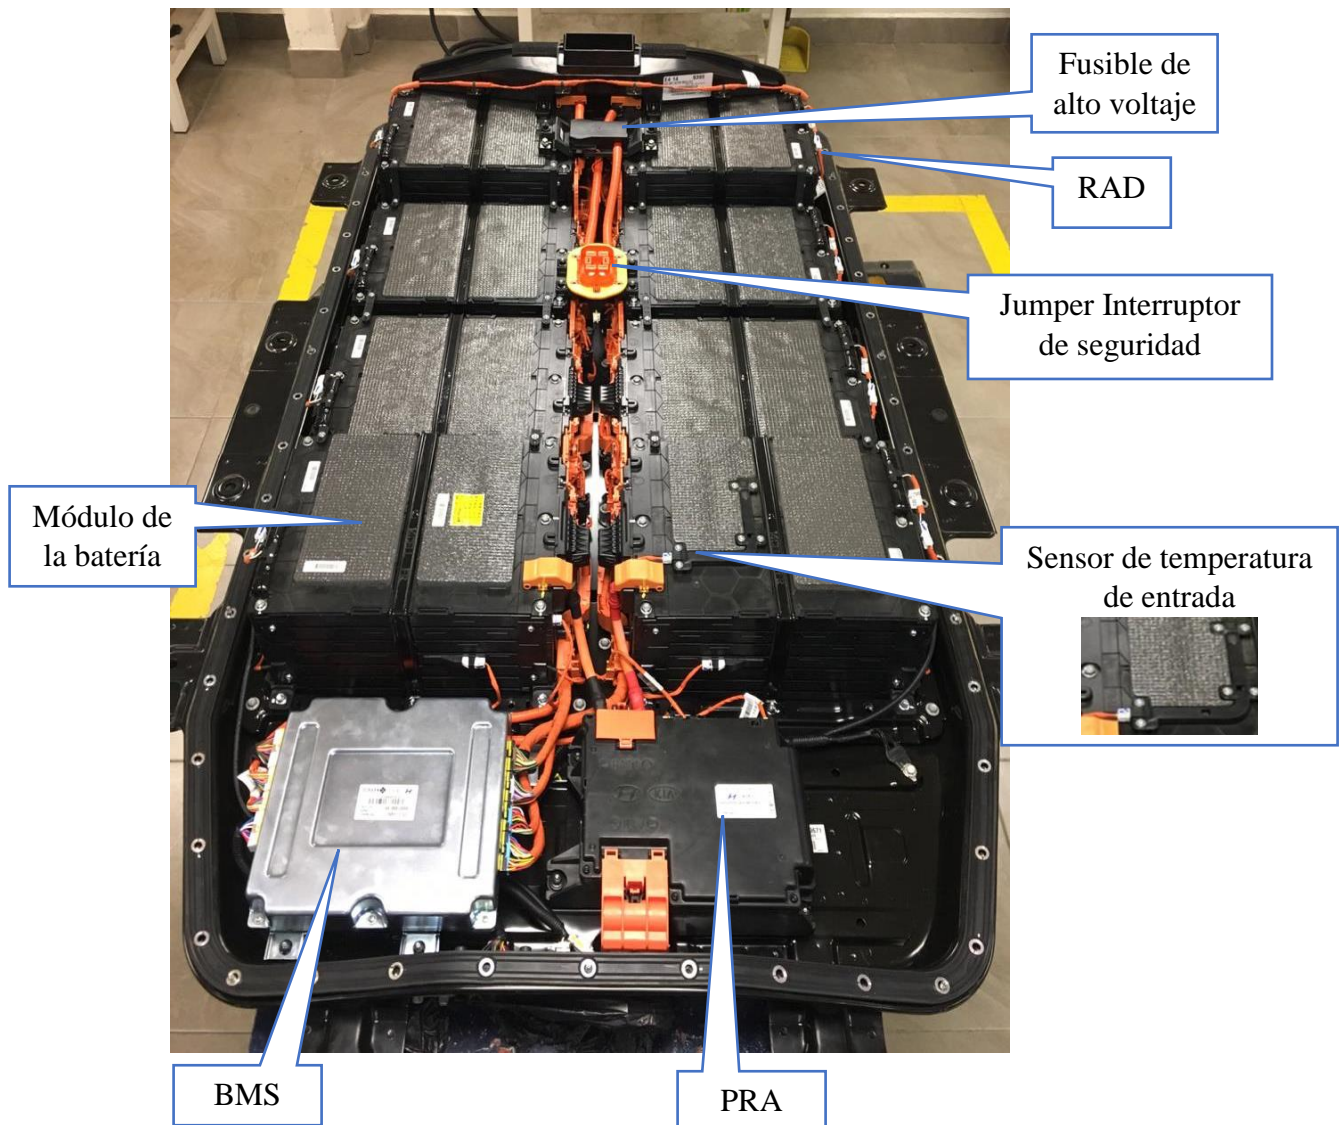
Paquete de batería de alta tensión: Fuente: Autores.
